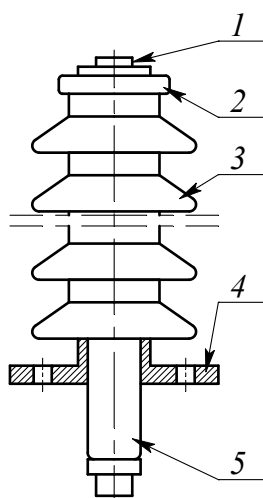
Бакелитовый ввод с полимерной крышкой: 1 – токоведущий стержень; 2 – верхний колпачок; 3 – крышка из силиконовой резины (верхняя часть изолятора); 4 – средний фланец; 5 – нижняя (масляная) часть изолятора
